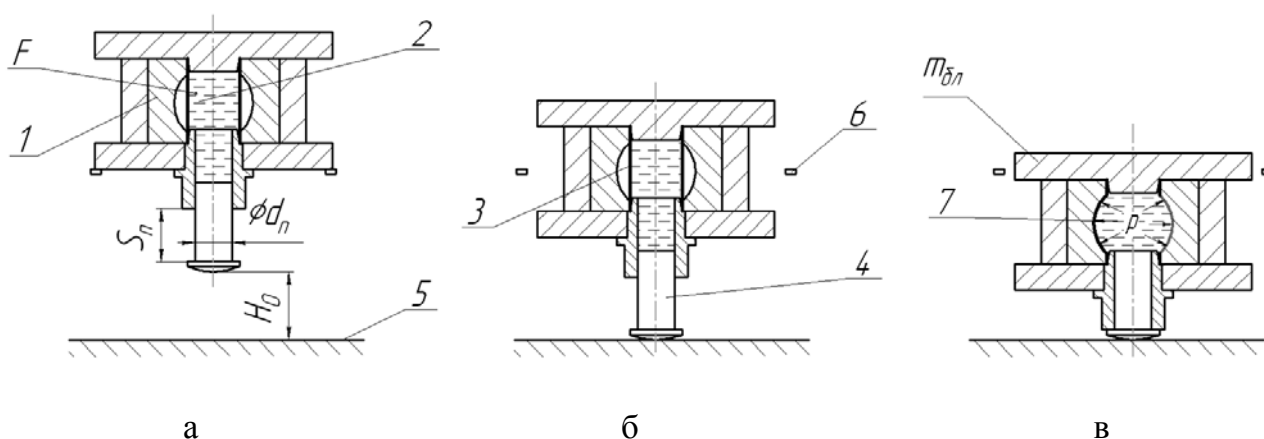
Кинематическая схема гравитационной гидродинамической штамповки: 1 – штамповый блок; 2 – передающая среда; 3 – заготовка; 4 – поршень; 5 – жесткая опора; 6 – фиксаторы; 7 – отштампованная деталь; F – формующая камера; d_n – диаметр поршня; S_n – ход поршня; H_0 – расчетная исходная высота системы; $m_{бл}$ – масса штампового блока; p – давление внутри формующей камеры
